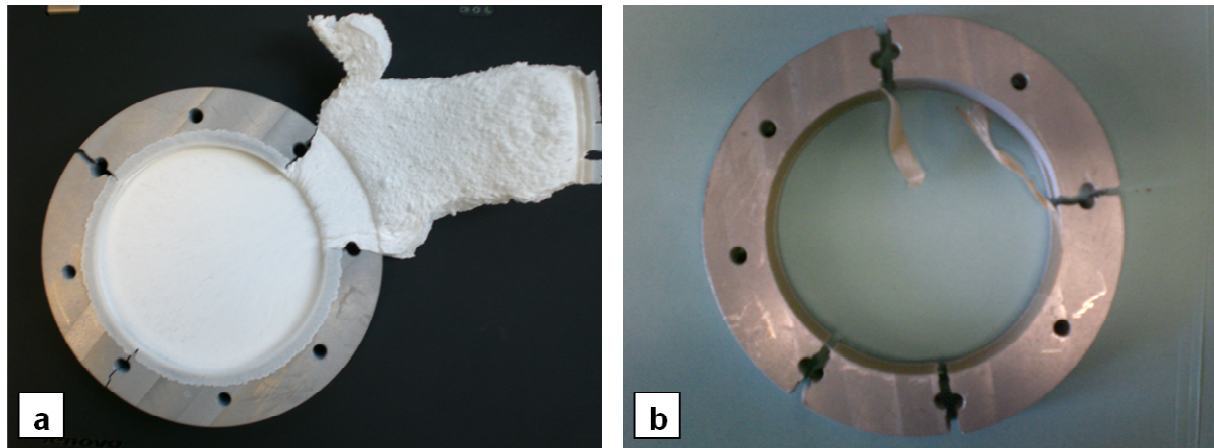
a) Aufsicht auf die geöffnete Form mit nach außen hin explosionsartig geschäumten Teilstück und b) geborstenem makroporösen Aluminiumring der Form.
